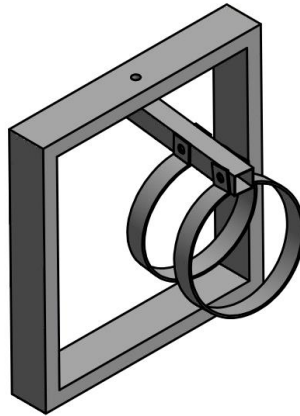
Assembly* Tungku Pelebur Aluminium
